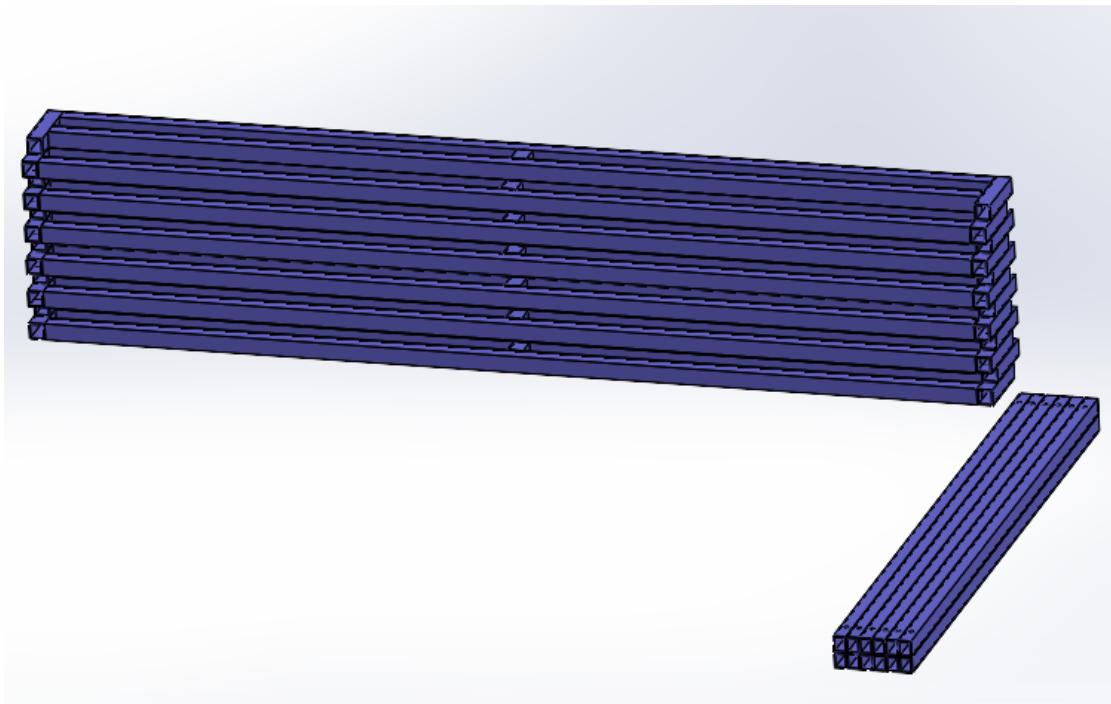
Les barres Transversale de la base et du support démontée et empilées les unes sur les autres.
